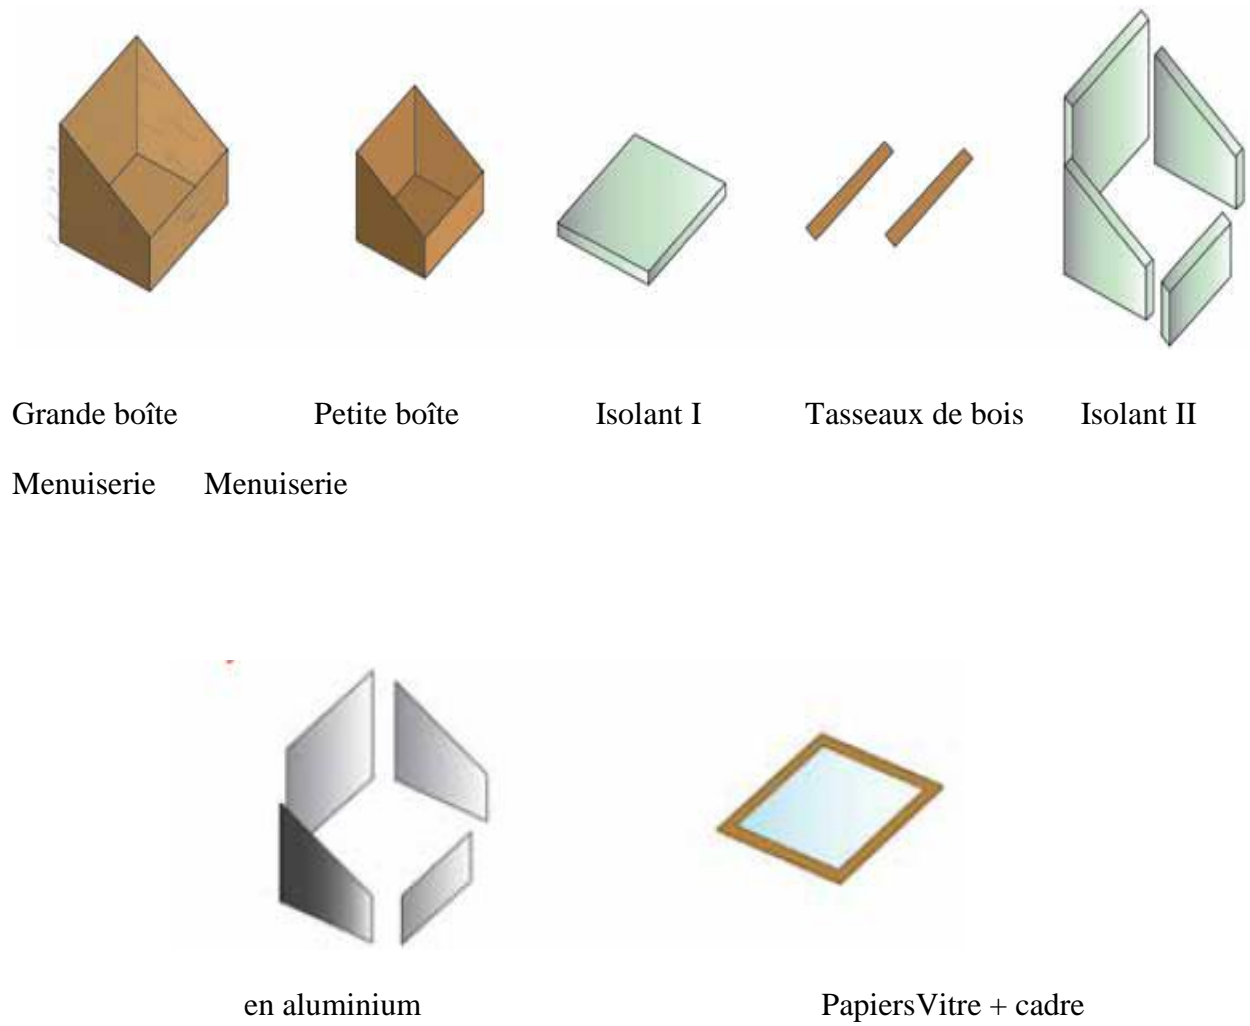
Matériaux nécessaires Pour installer la boîte
